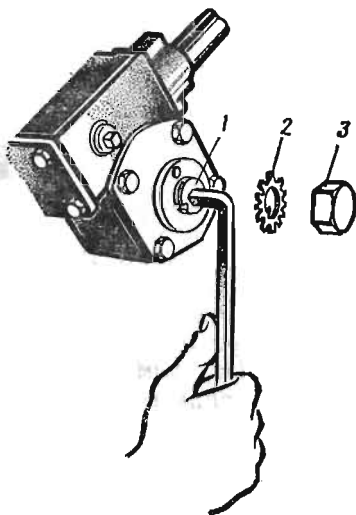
Регулировка зацепления ролика с червяком в рулевом механизме автомобиля ГАЗ-24 «Волга»
